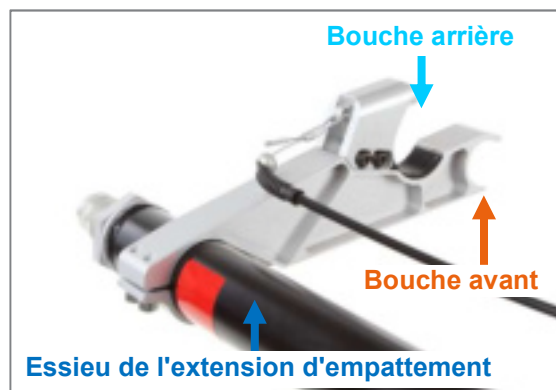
Vue d'ensemble des désignations pour l'allongement de l'empattement
